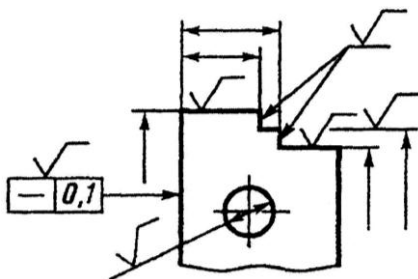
Пример расположения обозначений шероховатости поверхности
